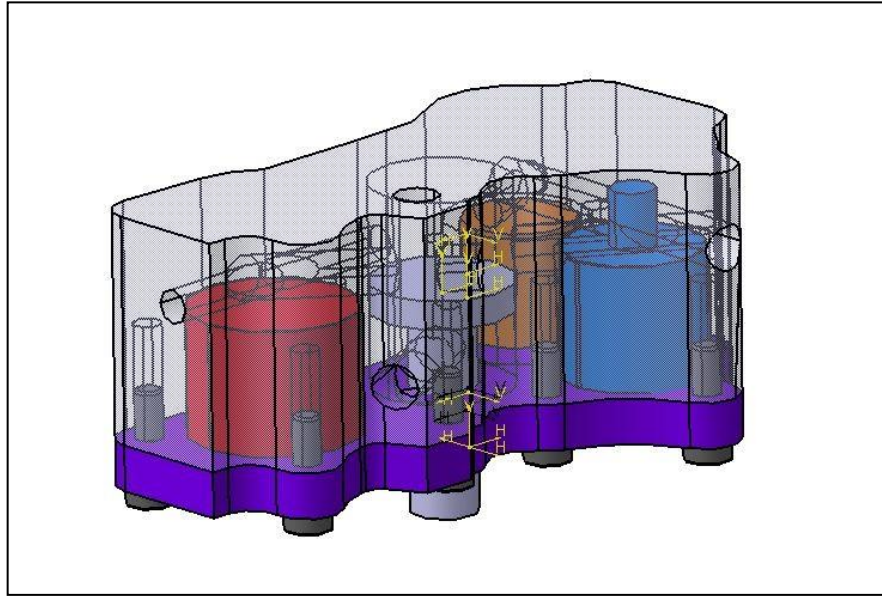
16 Aktüatör gövdesi montaj gurubu parçaları
